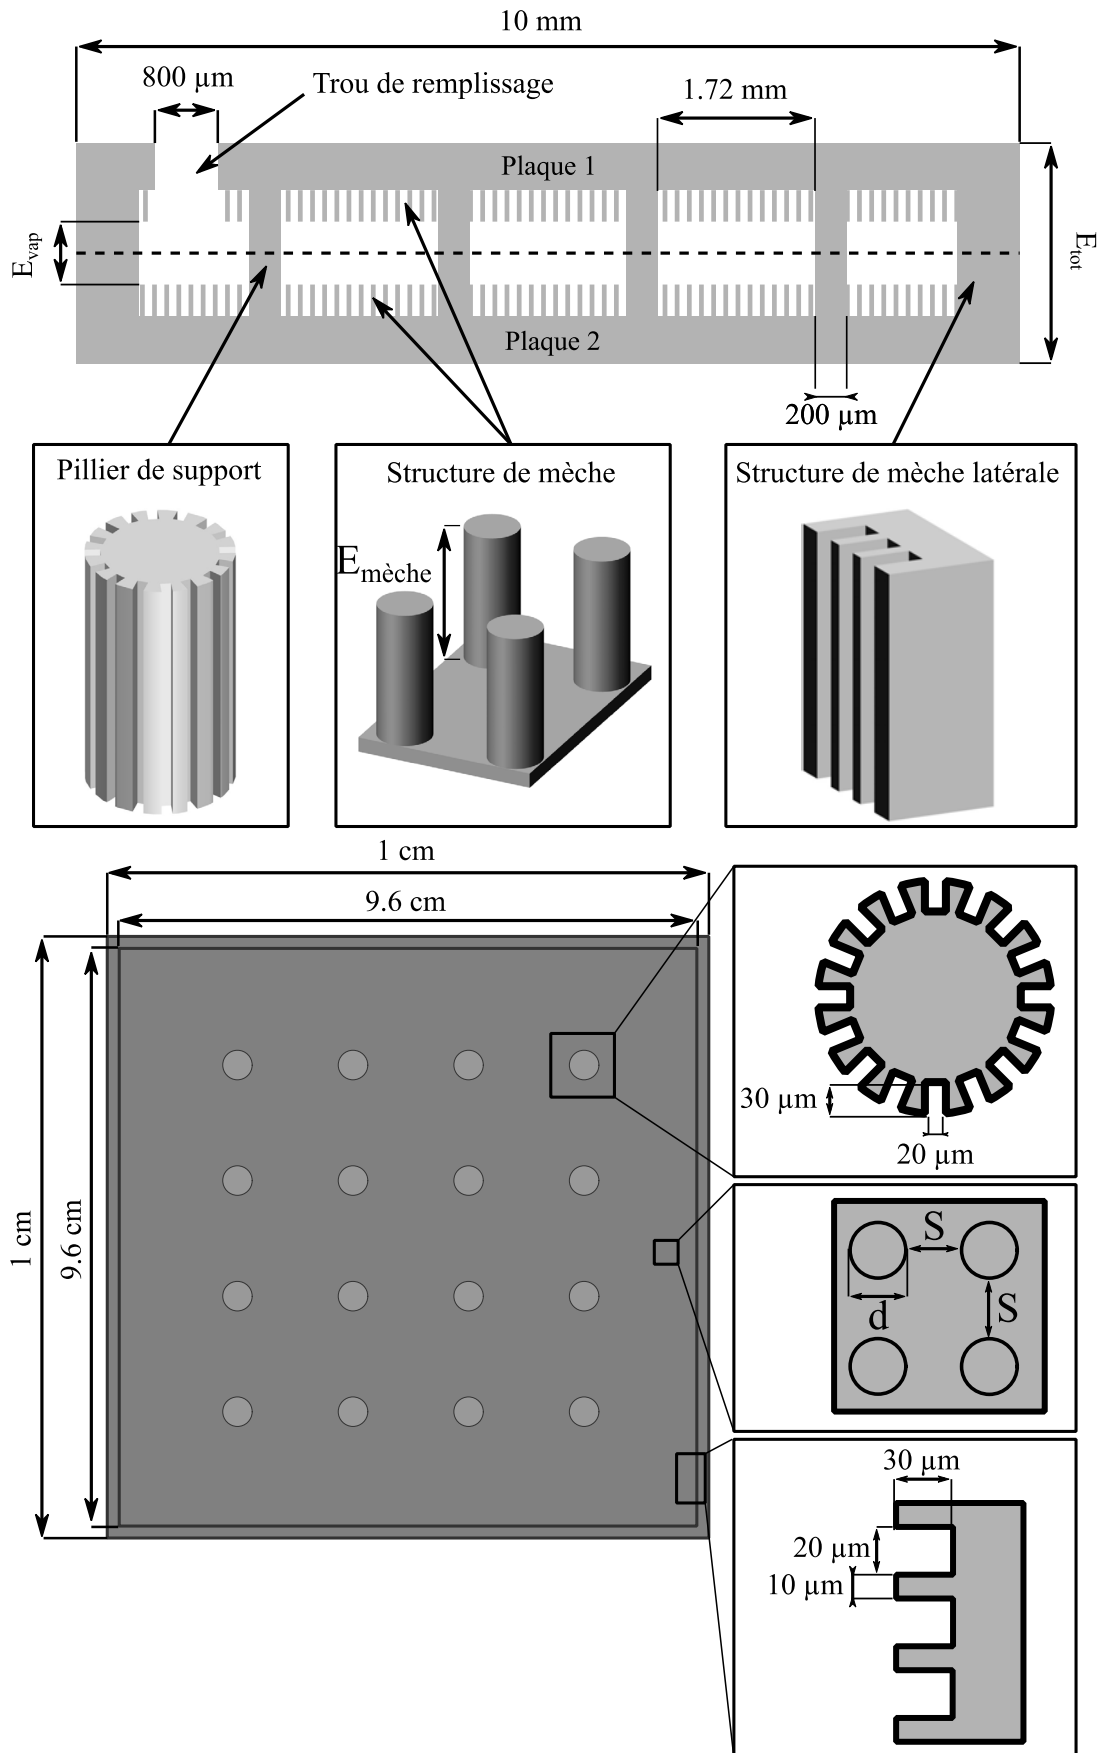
Description détaillée du prototype de chambre à vapeur avec trou de remplissage en vue de coupe et vue de dessus semi-transparente.
